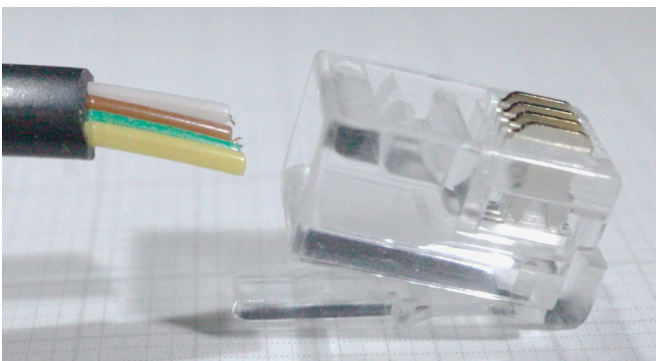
Motorstecker: Kabel in Modular 4P4 Stecker einführen - POLUNG !!!
